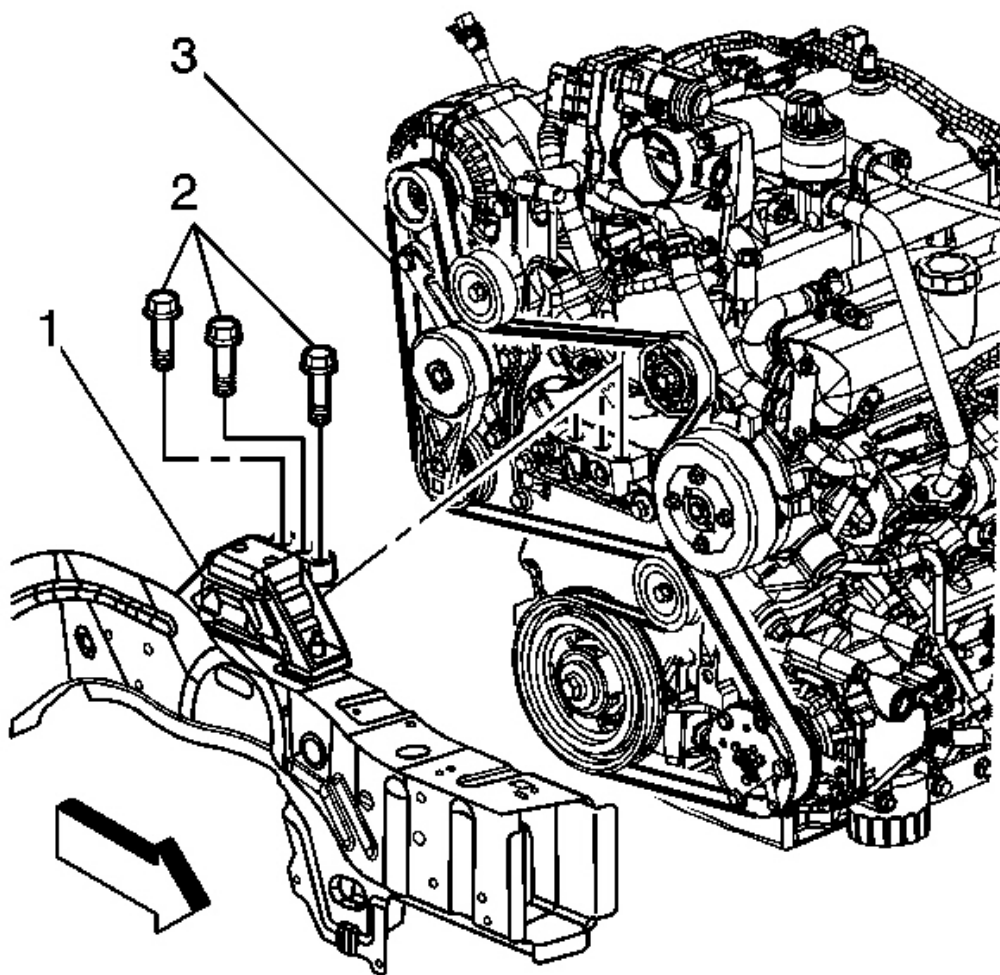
Vista de la izquierda Transeje Mount & Bolts
